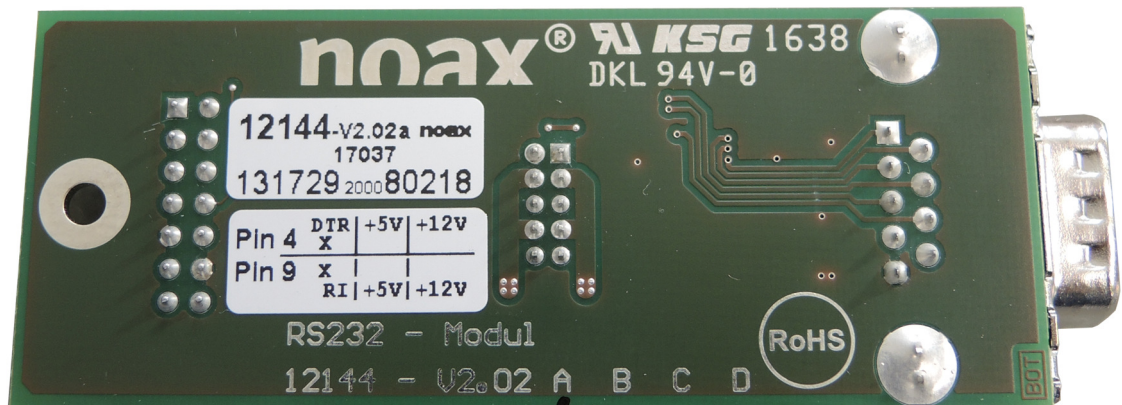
Rückseite RS232-Schnittstellenmodul mit Einstellungskennzeichnung (sichtbare Seite)
